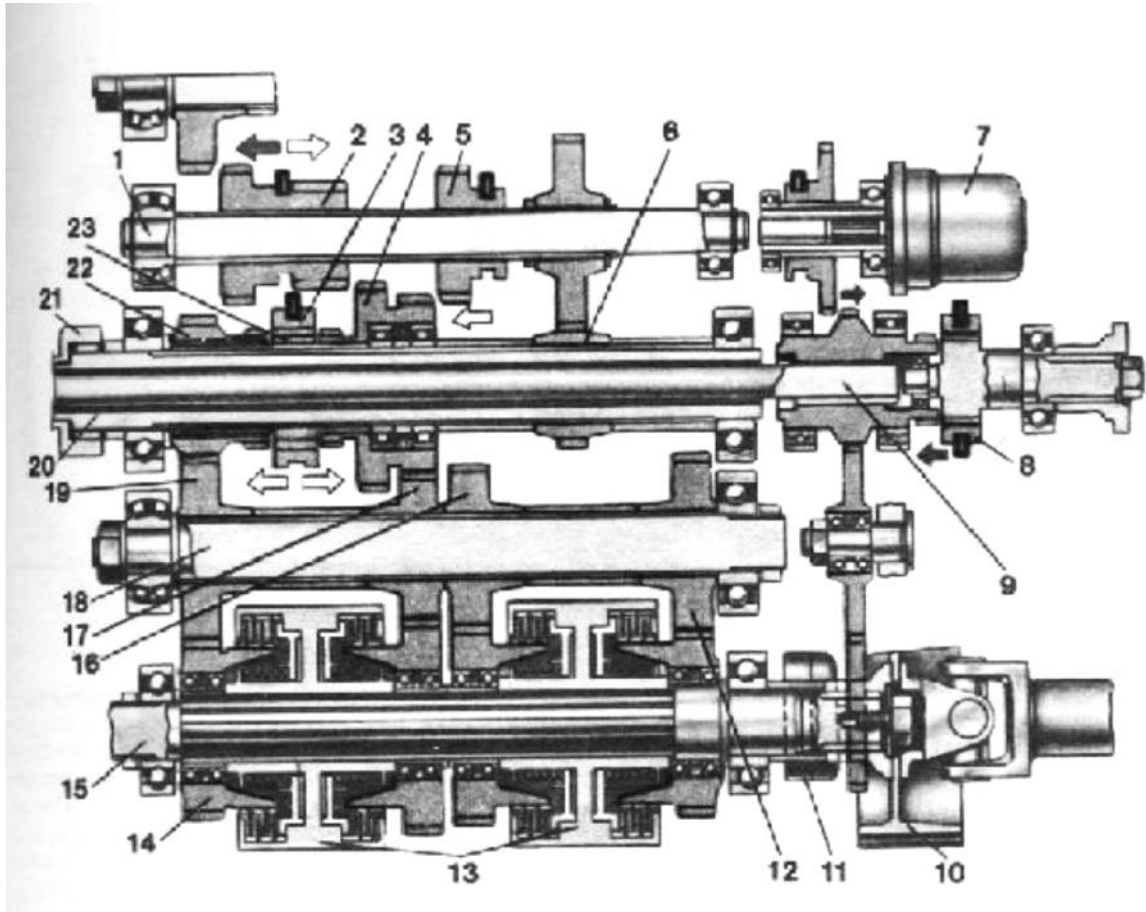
Схема коробки передач трактора ХТЗ-16131-03:
